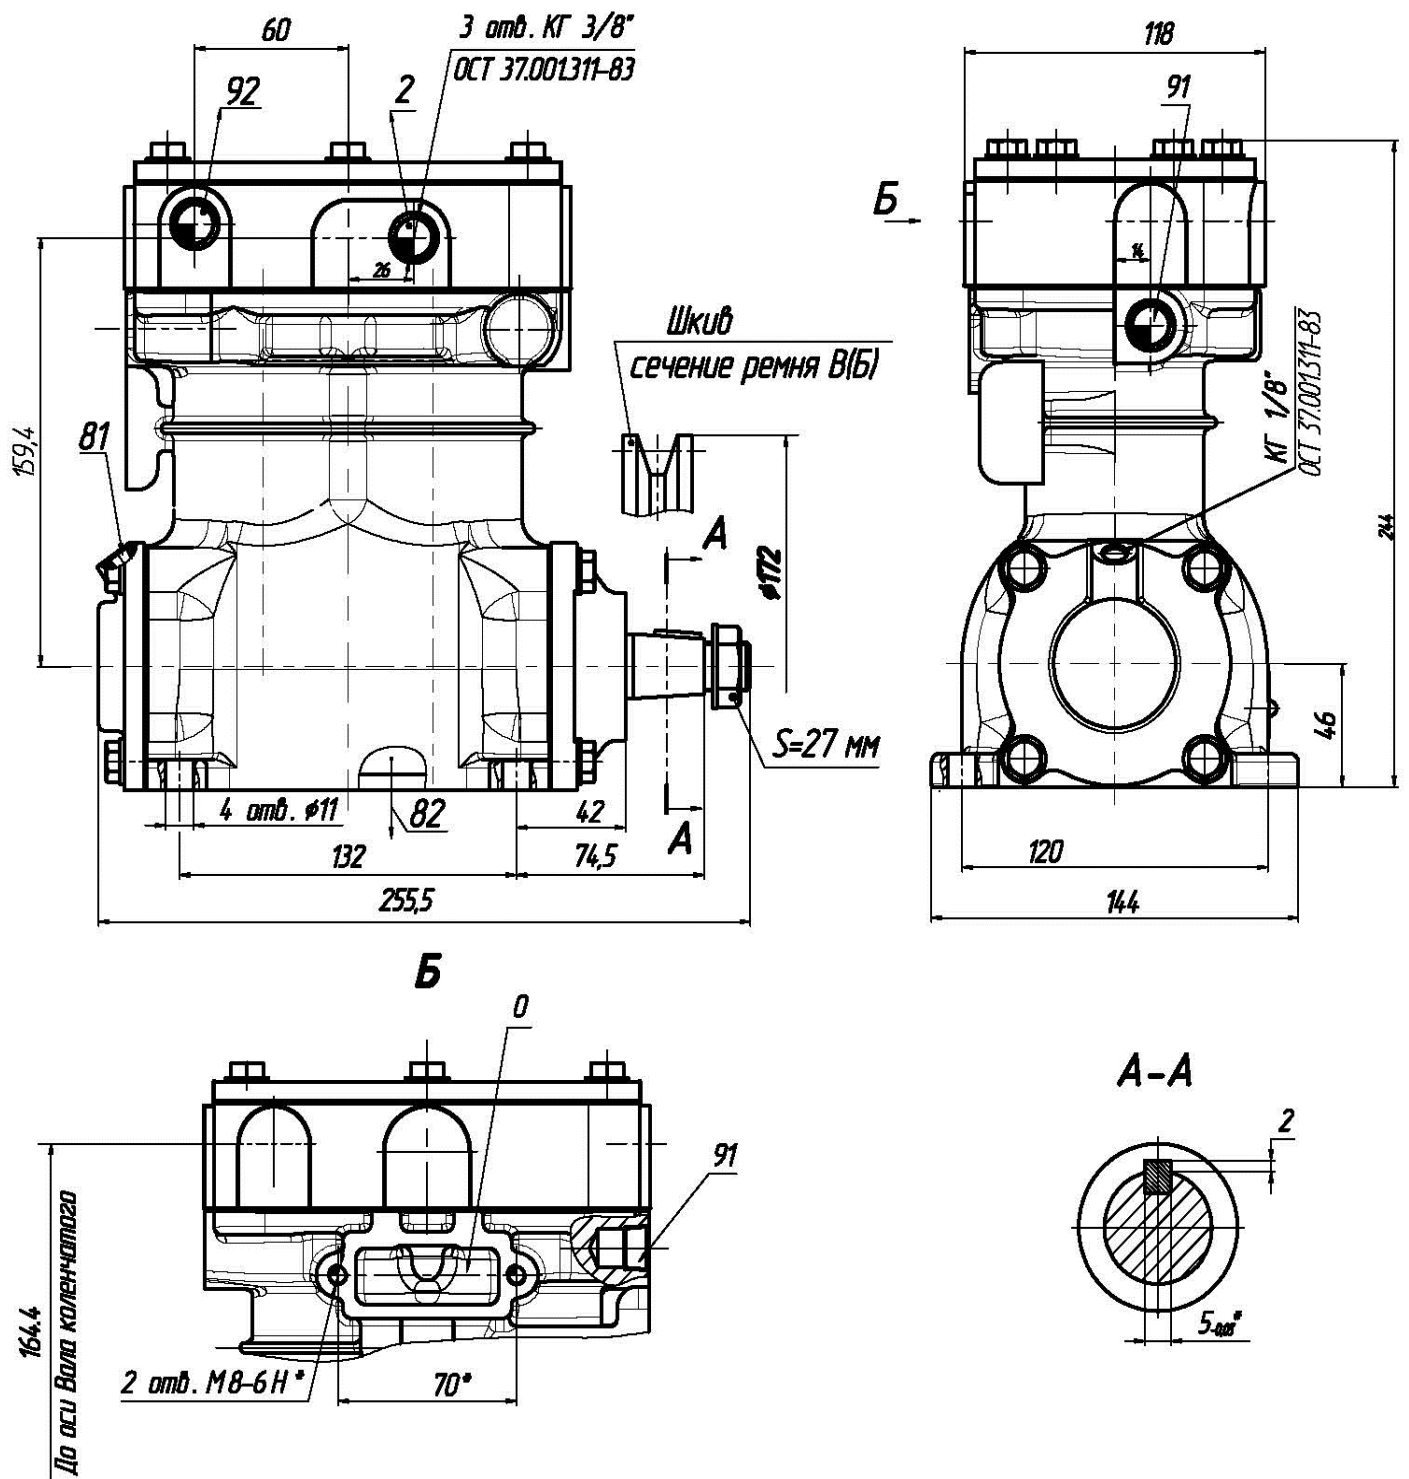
Присоединительные и установочные размеры компрессора АМ.3509012-16.
